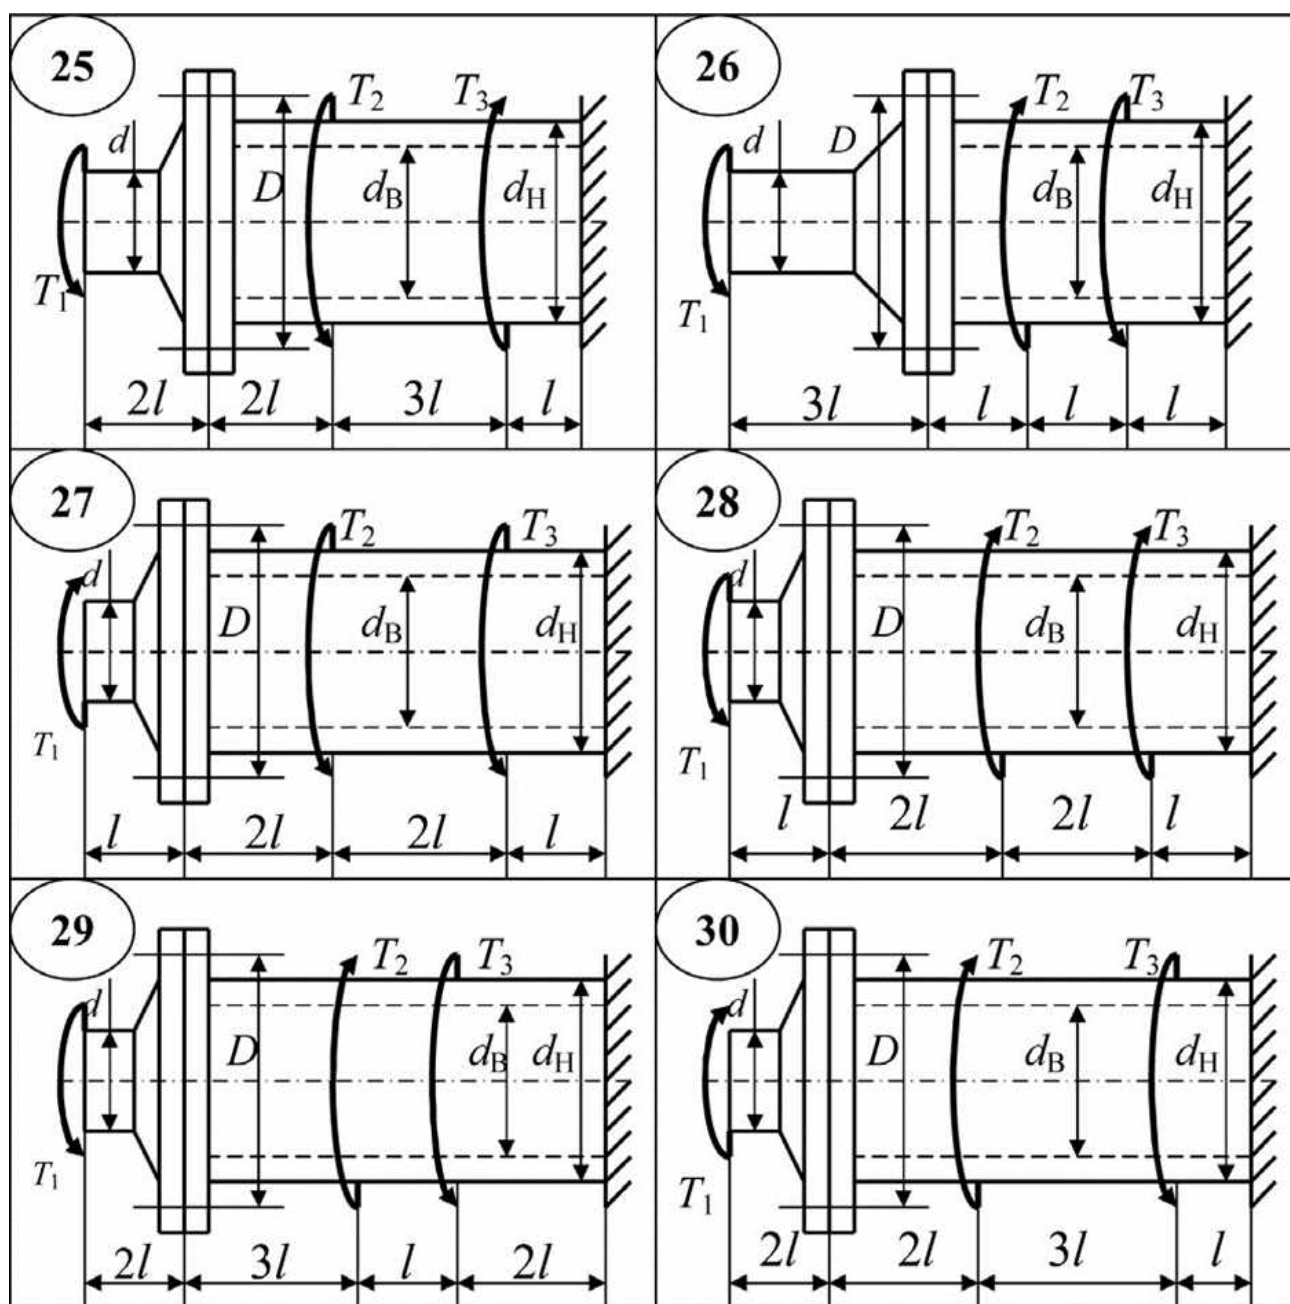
Варианты расчетных схем (25–30) задание 2
